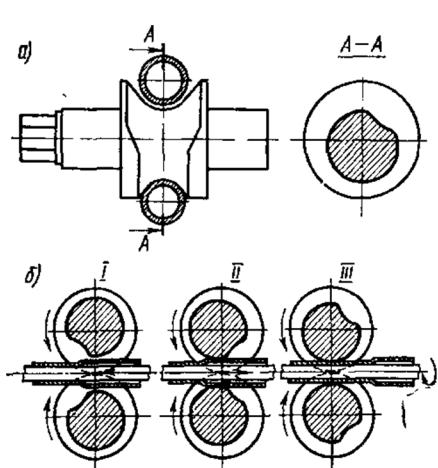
Схема пилигримовой прокатки за один оборот валков:
